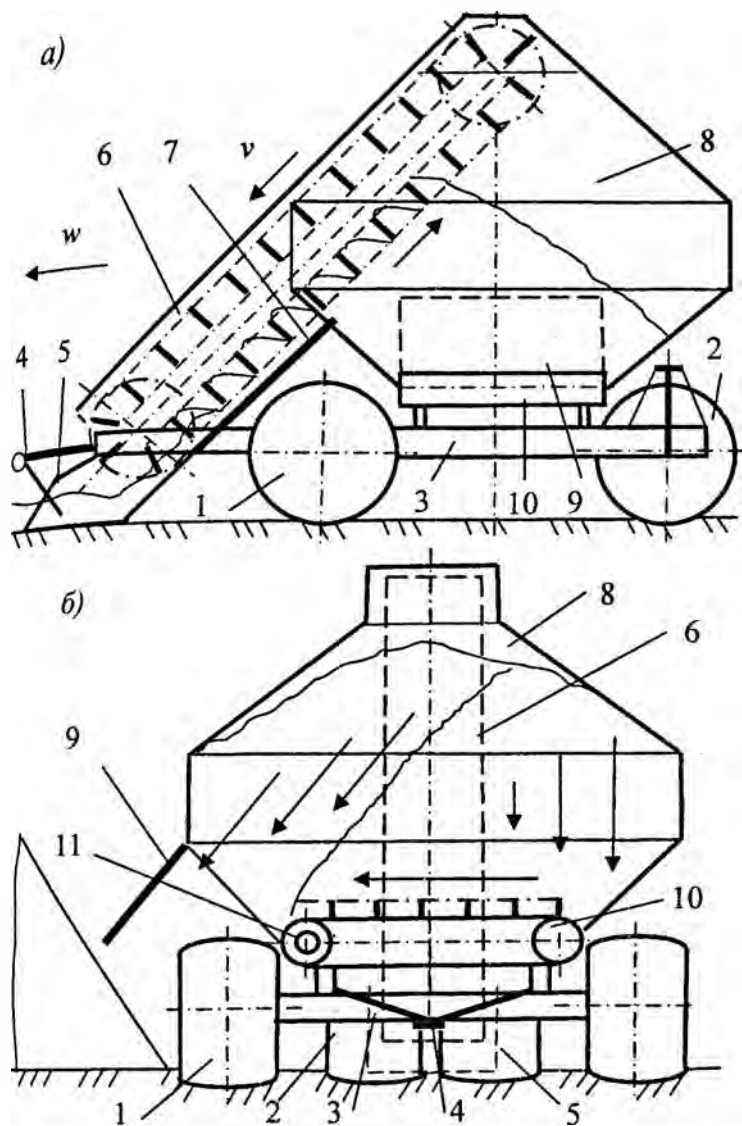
Колесная машина для уборки фрезерного торфа с передним расположением скрепера и грузозачного конвейера
